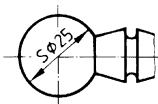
Kugelform (Maßlinie mit 2 Pfeilen)
